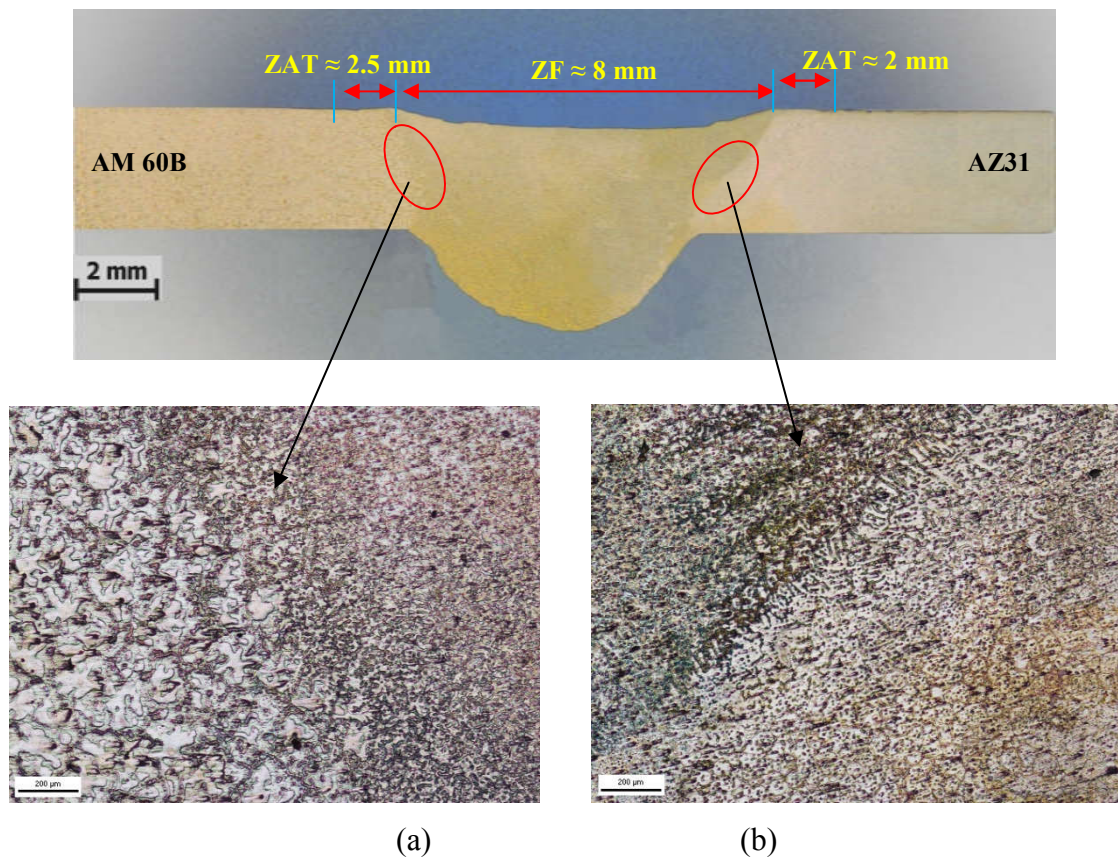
Macrographie des différentes zones du joint soudé (a)AM60 B, (b) AZ31.
